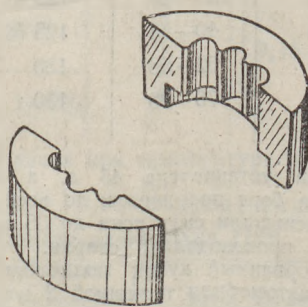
Подставка для разборки роликового подшипника ступицы заднего колеса.
